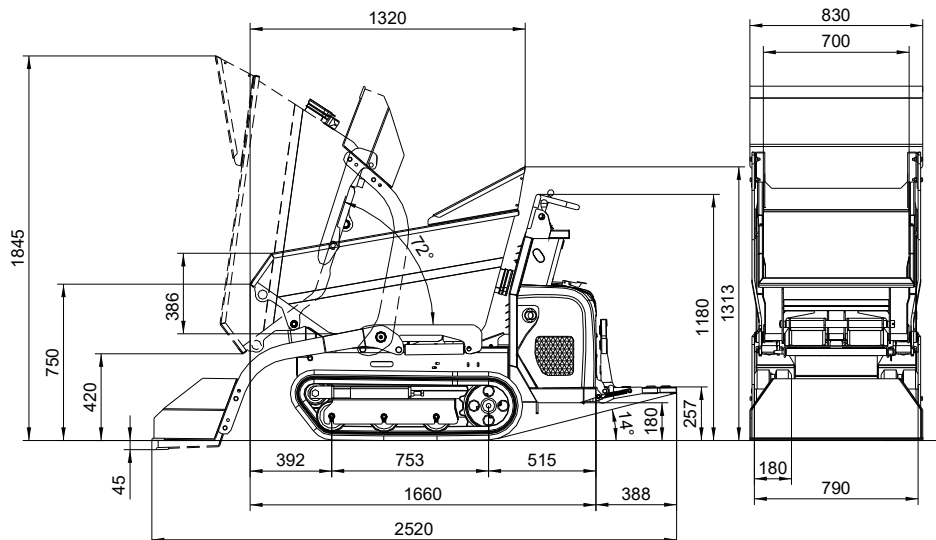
Dimensions de la machine (modèle DT08-P avec benne)
